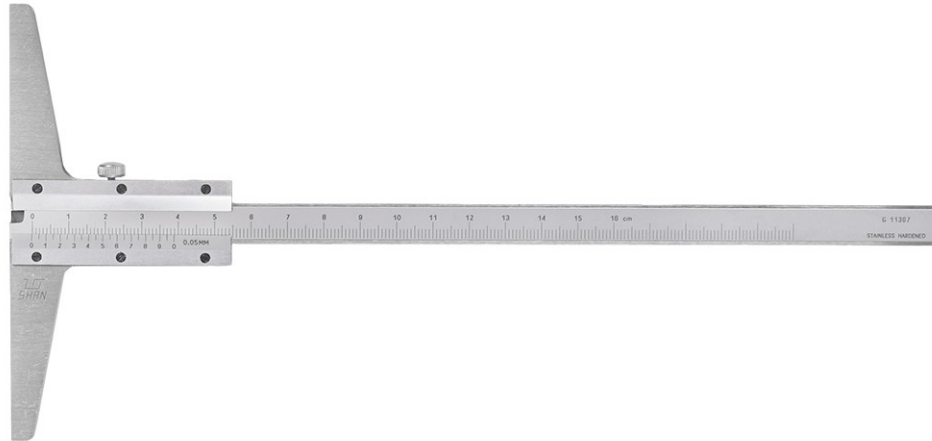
Общий вид штангенглубиномеров ШГ с прямой штангой
